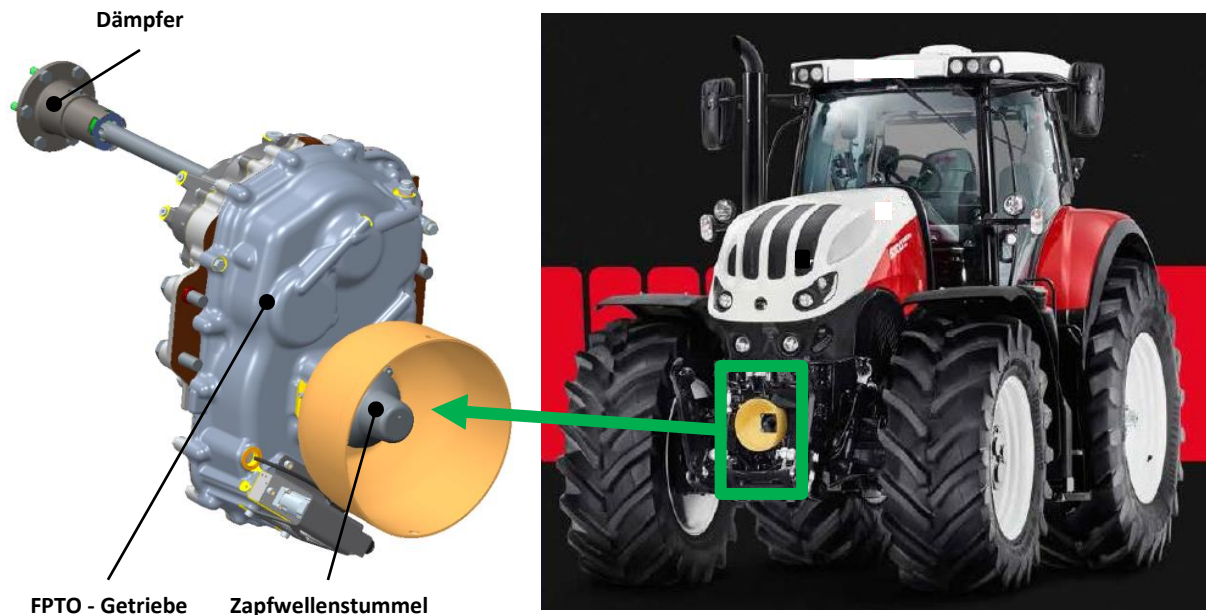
Einbauposition des FPTO – Getriebes [2]
